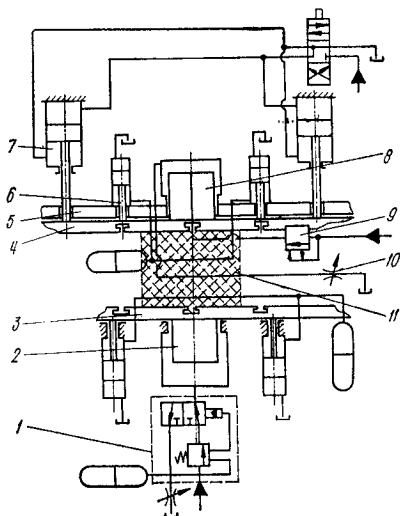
Схема привода с двусторонним уплотнением заготовки.
